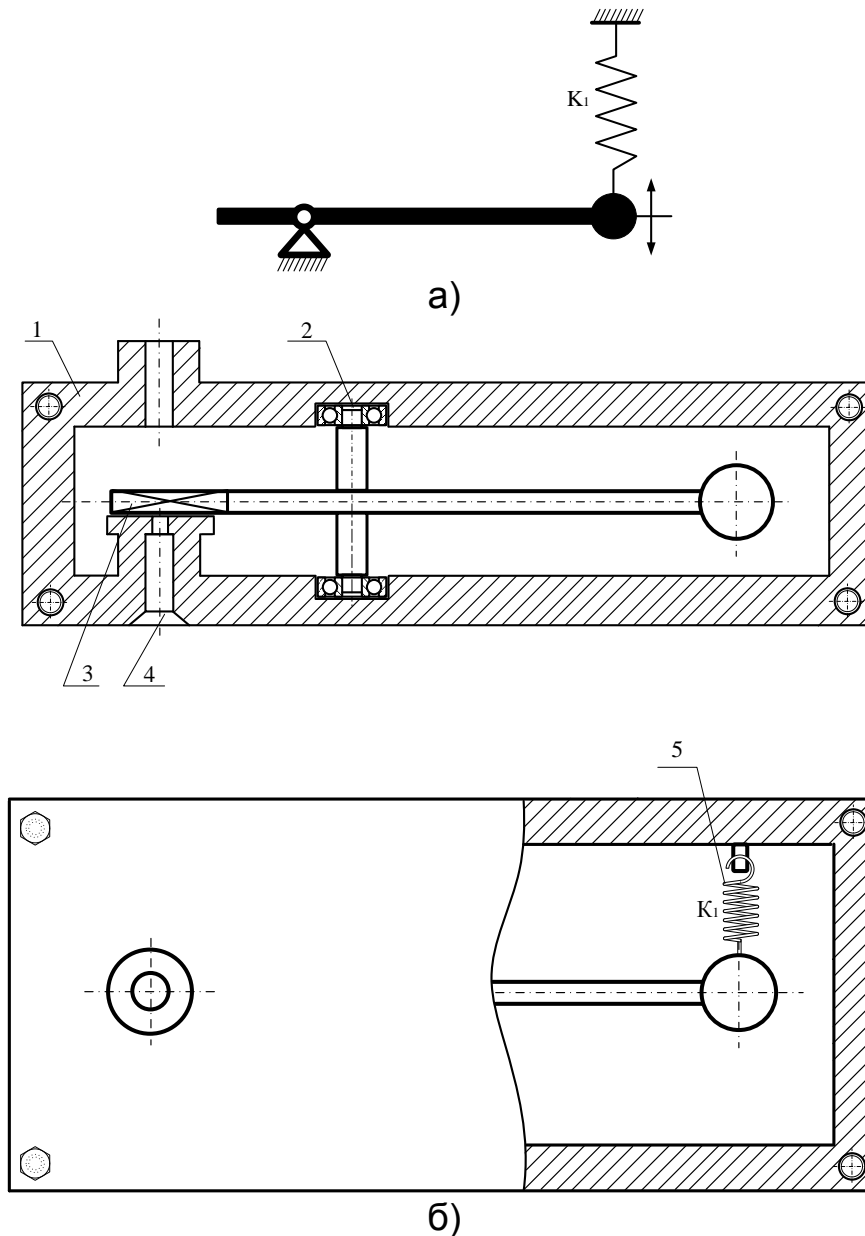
Дросельний резонаторний пристрій пневматичної системи віброзахисту: а) принципова розрахункова схема; б) конструктивна реалізація: 1 – корпус пристрою, 2 – кронштейн, 3 – важіль-заслінка, 4 – сопло, 5 – пружина.
